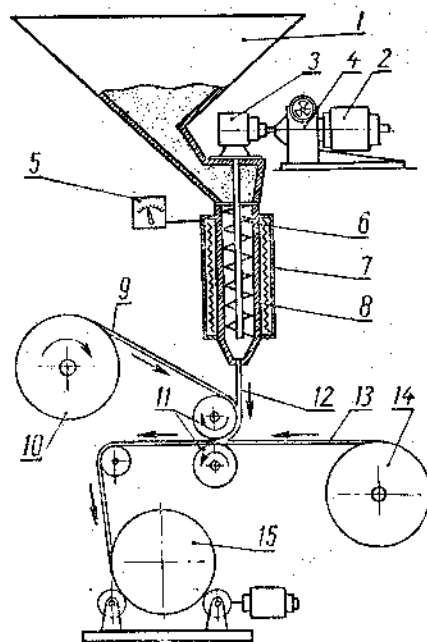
Сварочная машина для сварки тонких листов или пленки расплавленным прутом:
